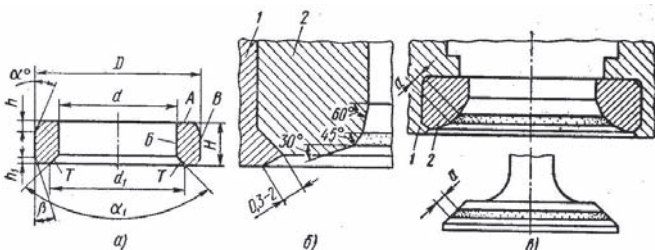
Седло клапана: а — рабочий чертеж; б — седло клапана, запрессованное в цилиндр двигателя; в — притертые рабочие поверхности седла и клапана; 1 — цилиндр двигателя; 2 — седло клапана; поверхность Т окончательно обрабатывают после запрессовки в головку (цилиндр) взаимное биение поверхностей Г и 23 не должно превышать 0,05 мм
